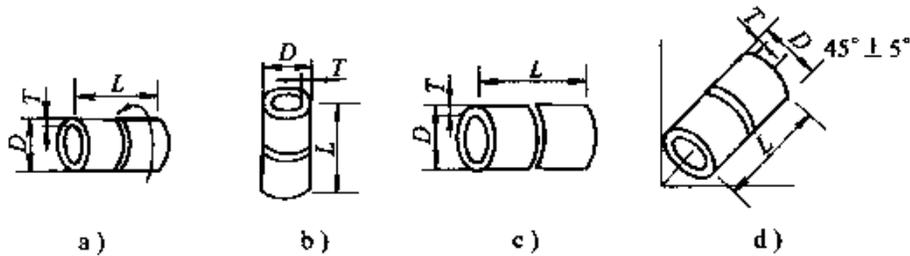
管状坡口对接焊缝试件 (TG)
